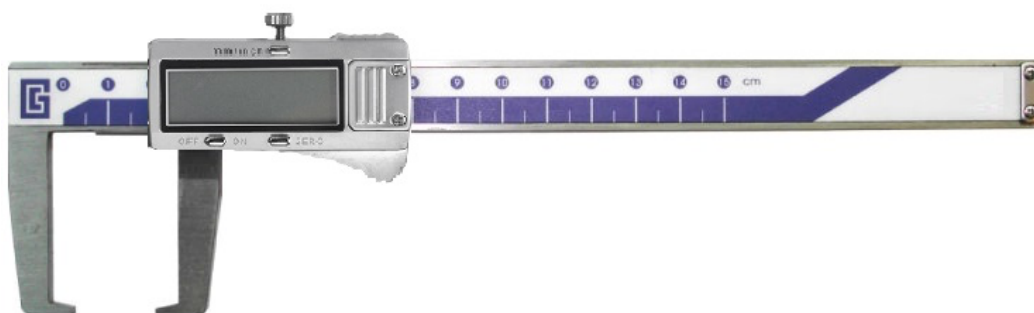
Общий вид штангенциркулей модели ШЦЦС-116
